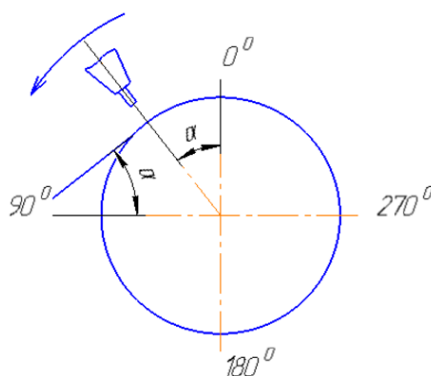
Положение сварочной ванны при орбитальной сварке неповоротного стыка против часовой стрелки
